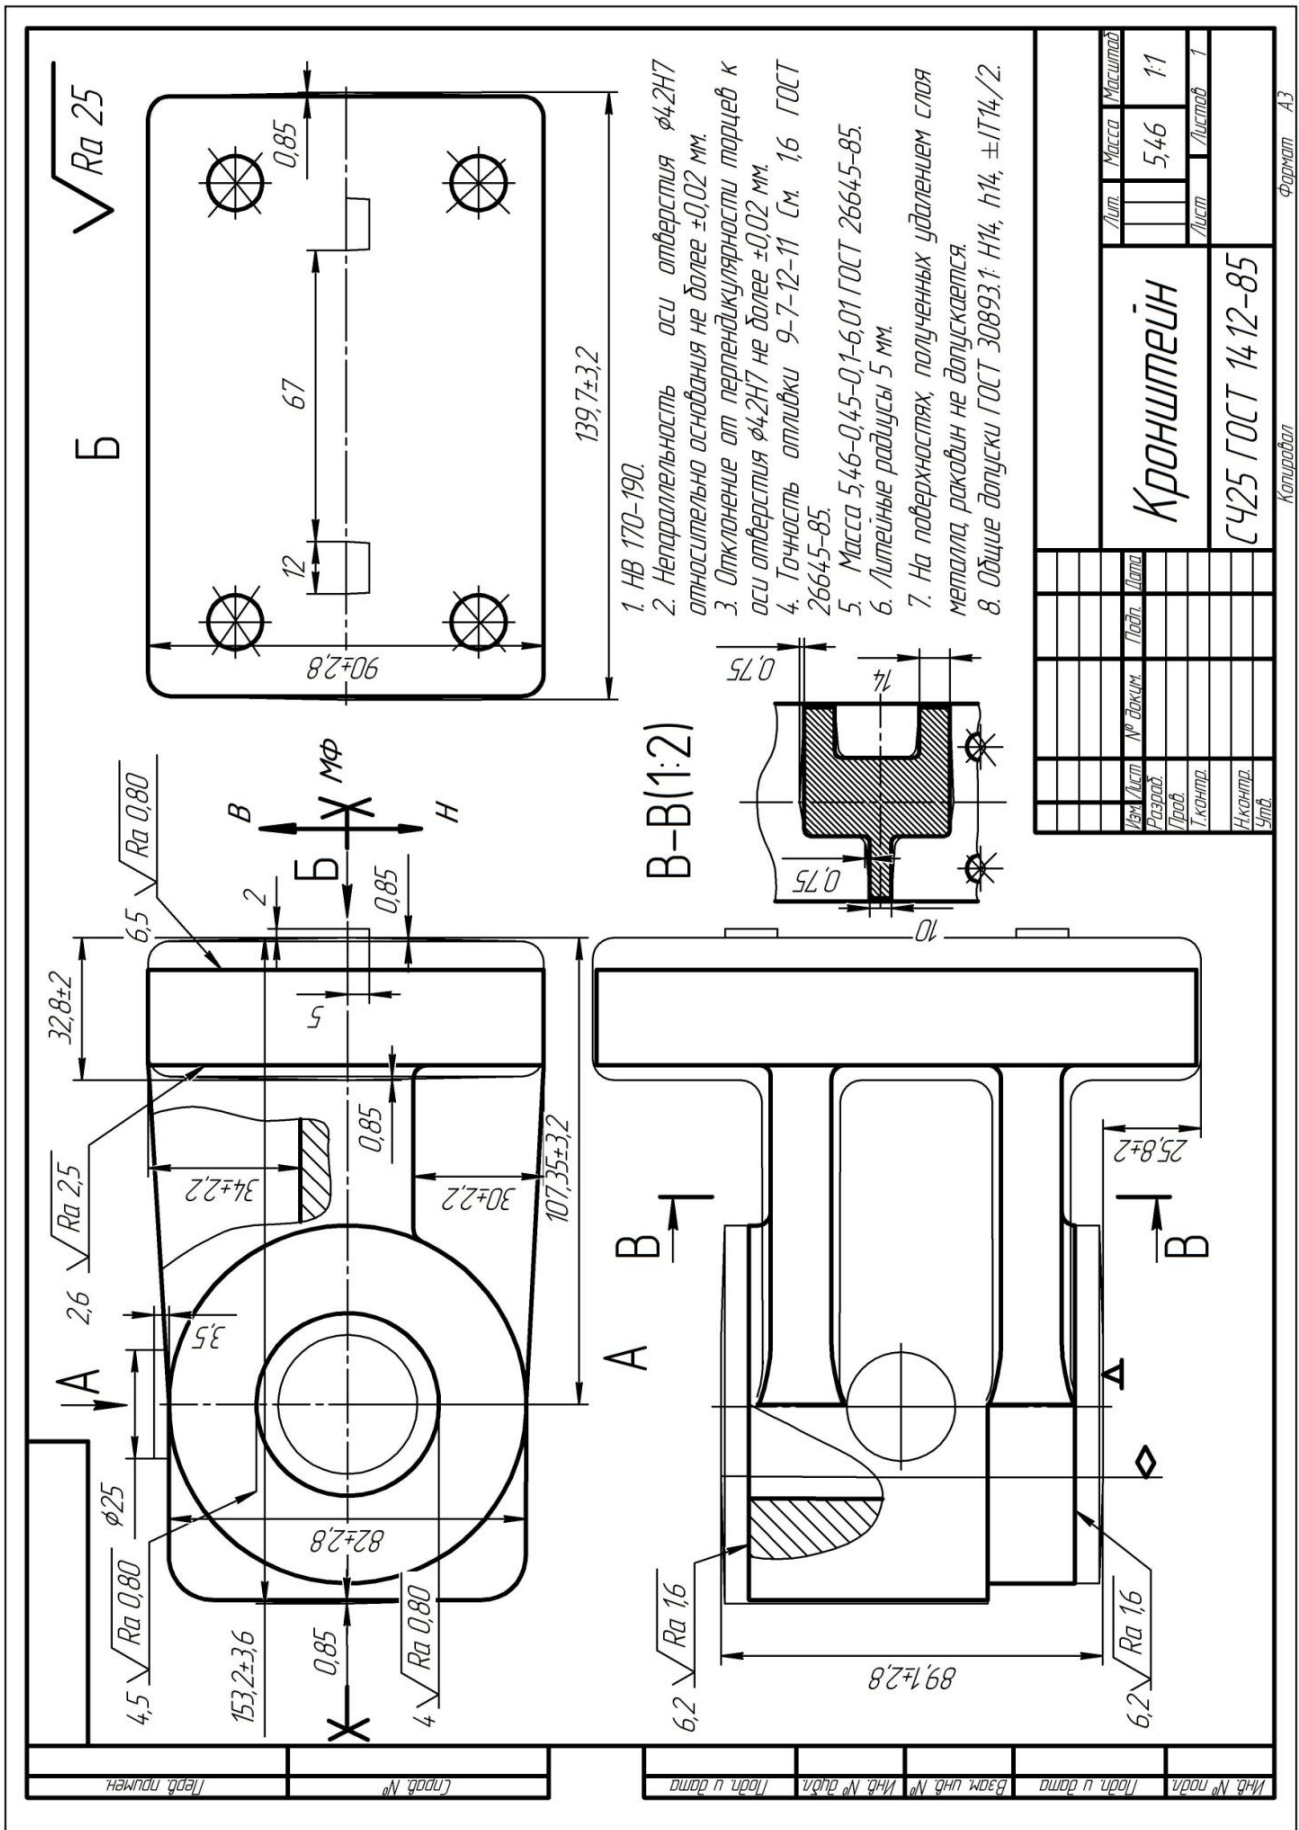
Чертеж отливки детали «Кронштейн»
